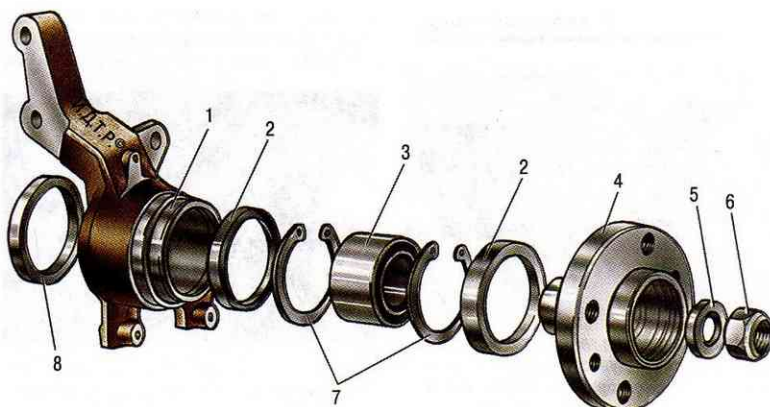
Поворотный кулак и детали ступицы переднего колеса: 1 — поворотный кулак; 2 — наружное грязеотражательное кольцо; 3 — подшипник ступицы; 4 — ступица колеса; 5 — упорная шайба; 6 — гайка; 7 — стопорные кольца; 8 — внутреннее грязеотражательное кольцо
